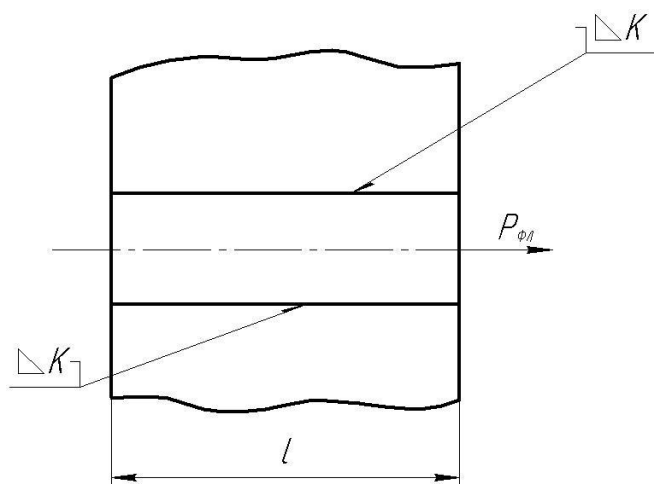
К расчёту сварочного шва.
